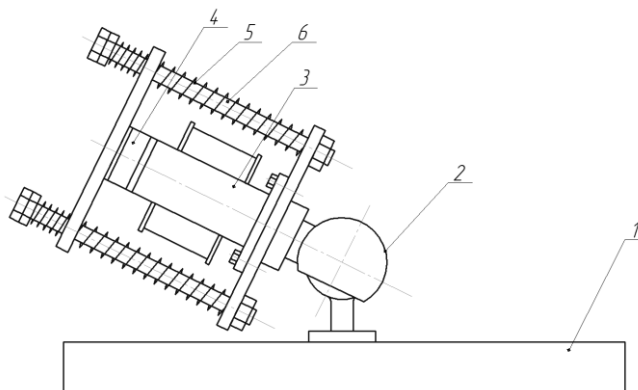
Конструктивна схема ВСПП: 1 – платформа; 2 - кульовий шарнір; 3, 4 - статор і якорь електромагнітного вібропривода, 5 - циліндричні пружини; 6 – напрямні
